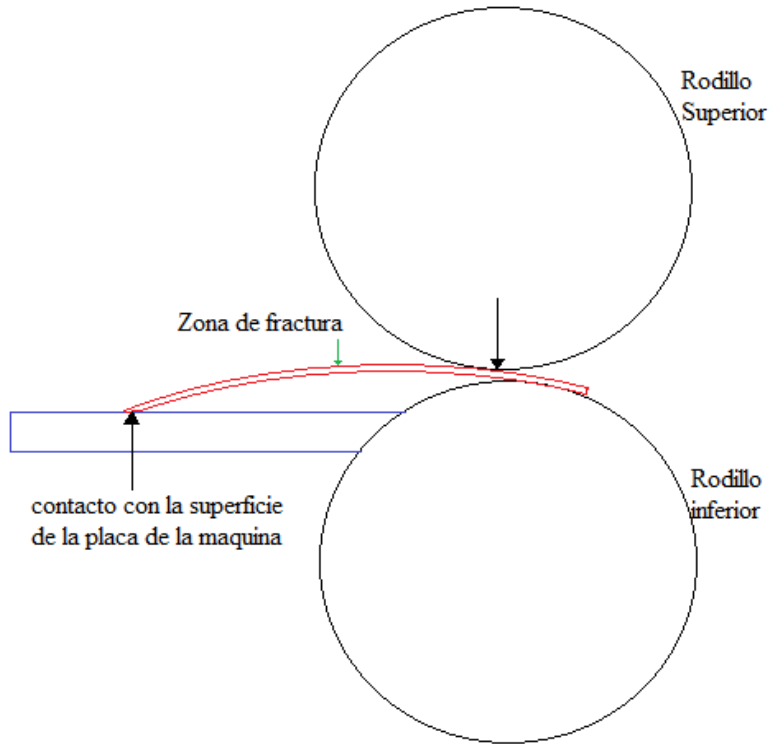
"Entrada cóncava hacia abajo que provoca fractura al contacto con la placa de la maquina" Fuente: Elaboración propia.
